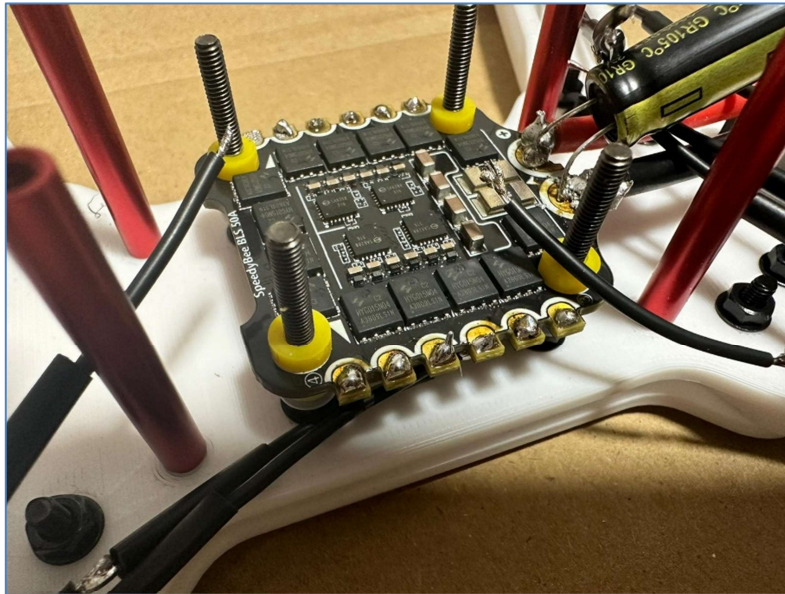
Cables de batería y condensador soldados al stack de PDB - ESC.
